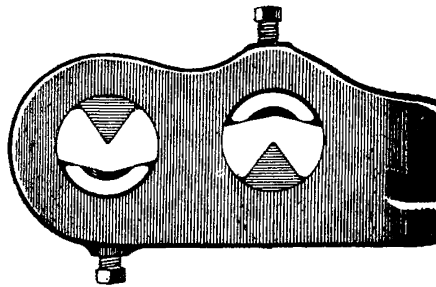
Крепление призм формы сектора в цилиндрических отверстиях рычагов.
